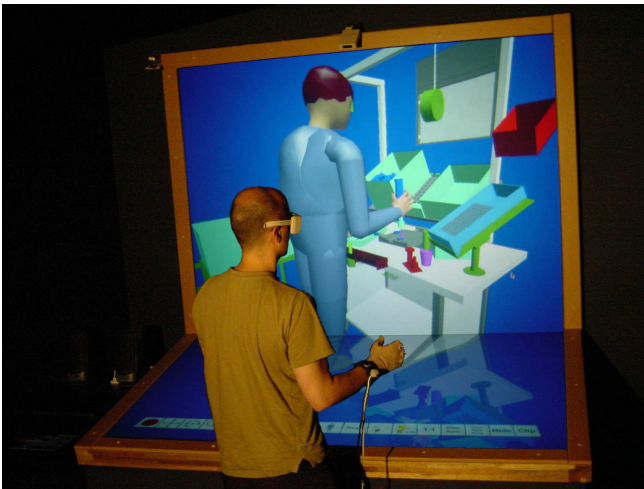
Schraubvorgang ist abgeschlossen – Werkzeug wird von Montagestelle entfernt
